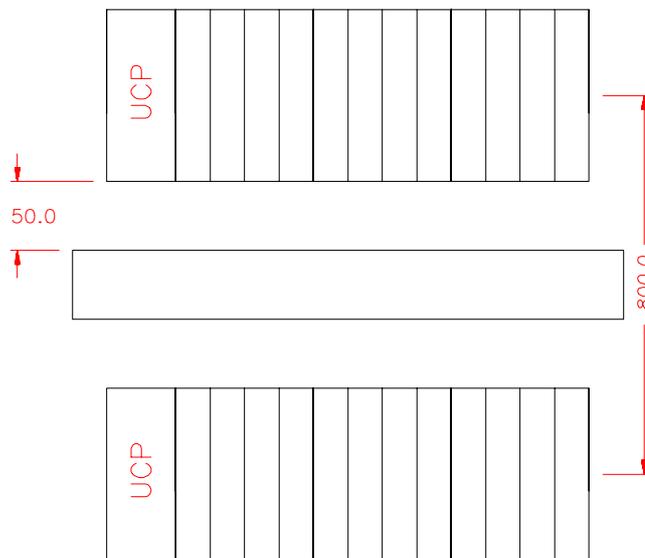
Dimensões Para Montagem Horizontal (mm)
